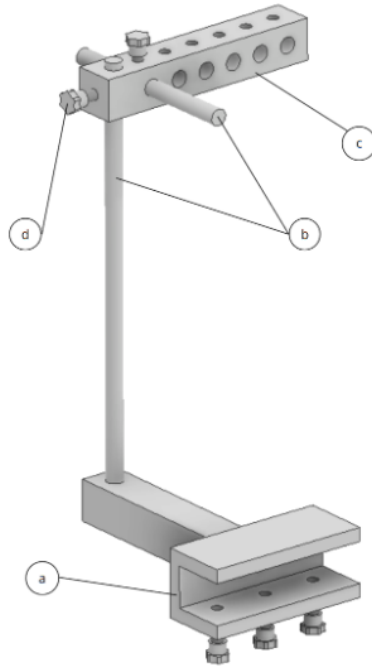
Modelo de la estructura metálica. a) Agarradera. b) Barras vertical y horizontal. c) Bloque de ajuste. d) Tornillos palometa
